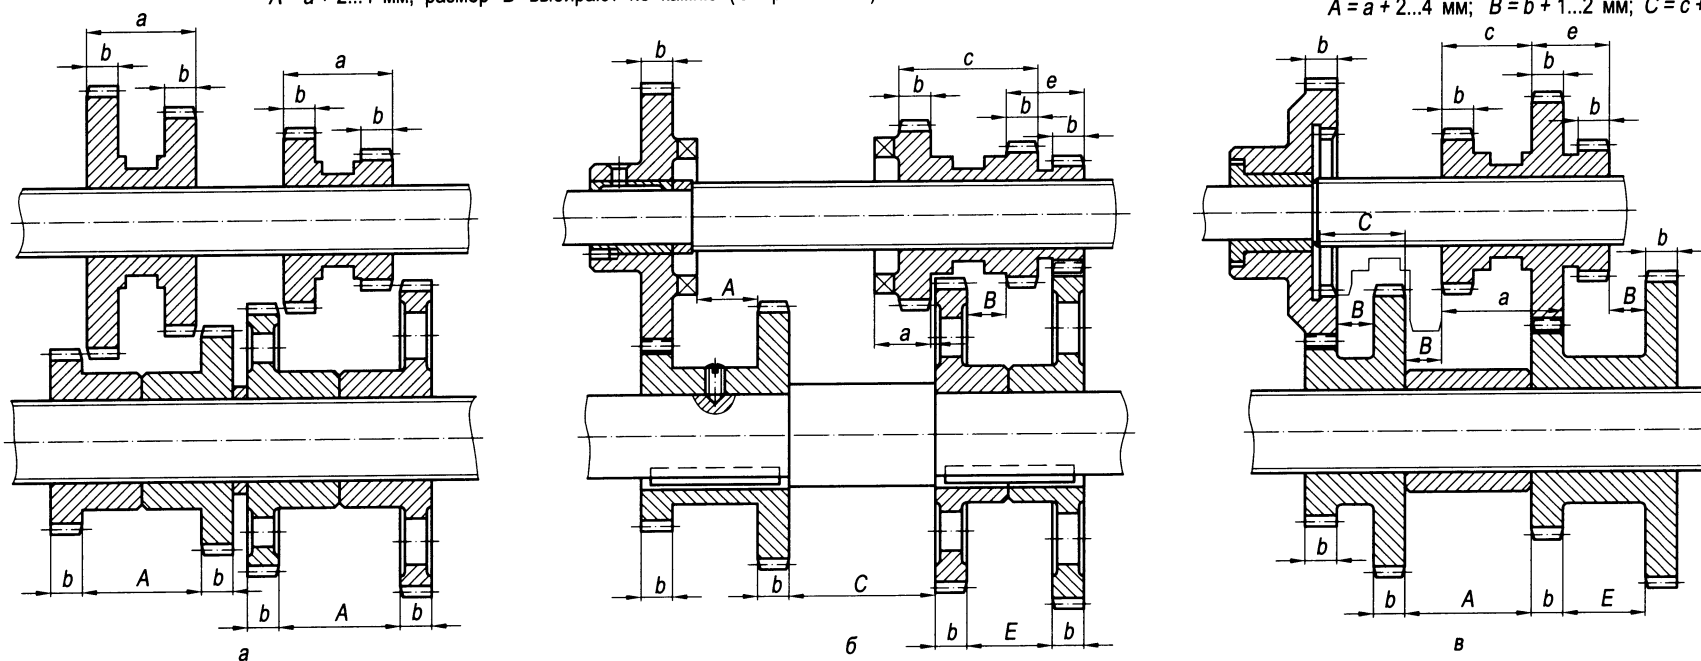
Основные размеры передвижного блока зубчатых колес четырехступенчатой коробки передач:
